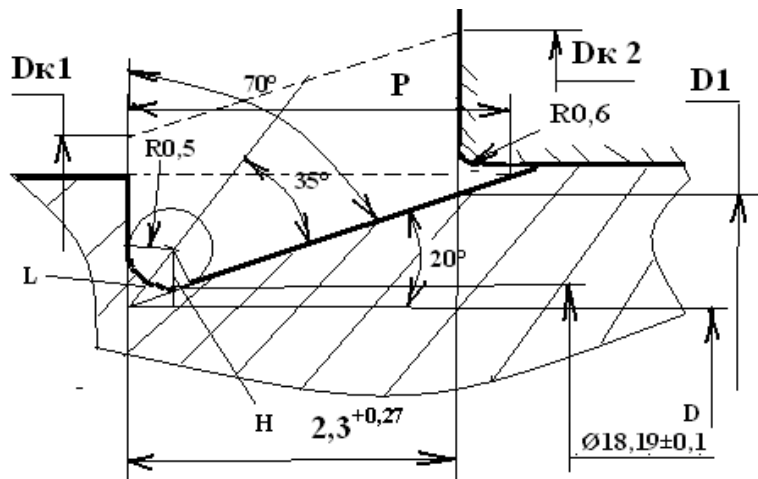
Канавка на шестерни под установку стопорного кольца
